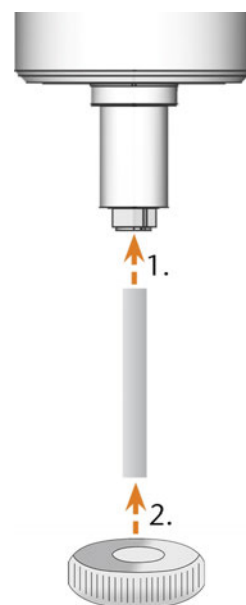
SVITAMENTO DELLA PINZA DI SERRAGGIO
